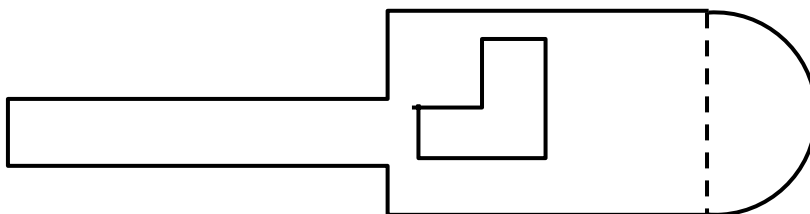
Prinzipieller Blechschnitt des Schiebbestücks
